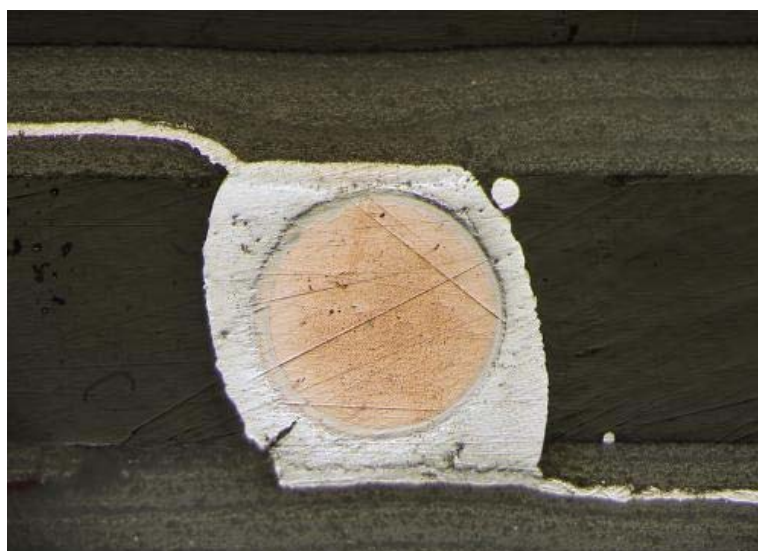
Detail pájeného spoje mezi „dimpled“ LTCC s pájecími kuličkami s Cu jádrem
